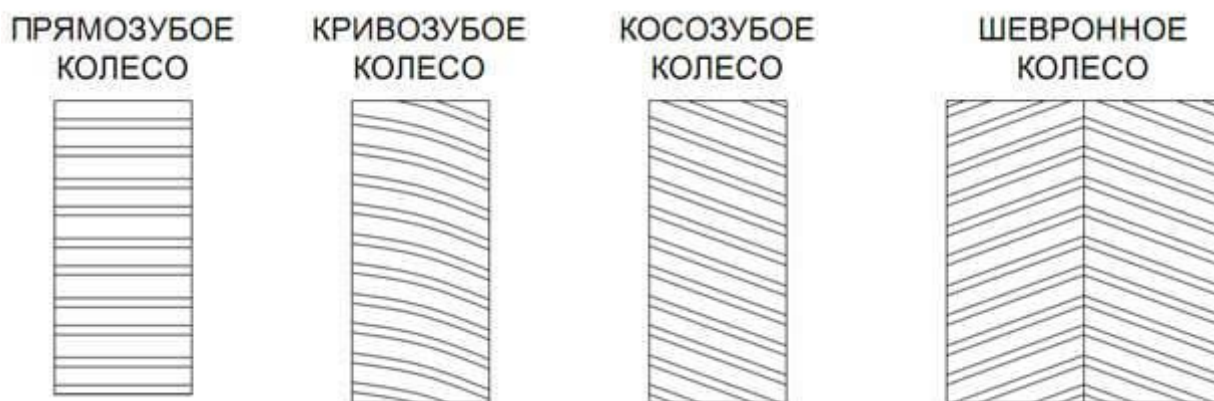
Типы зубьев колёс в цилиндрическом редукторе
